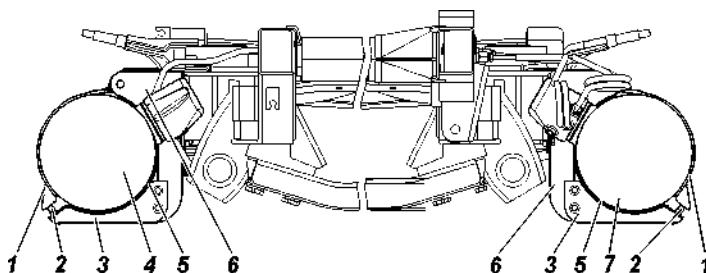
Установка газовых баллонов на автомобили УАЗ-236322, УАЗ-236324:
